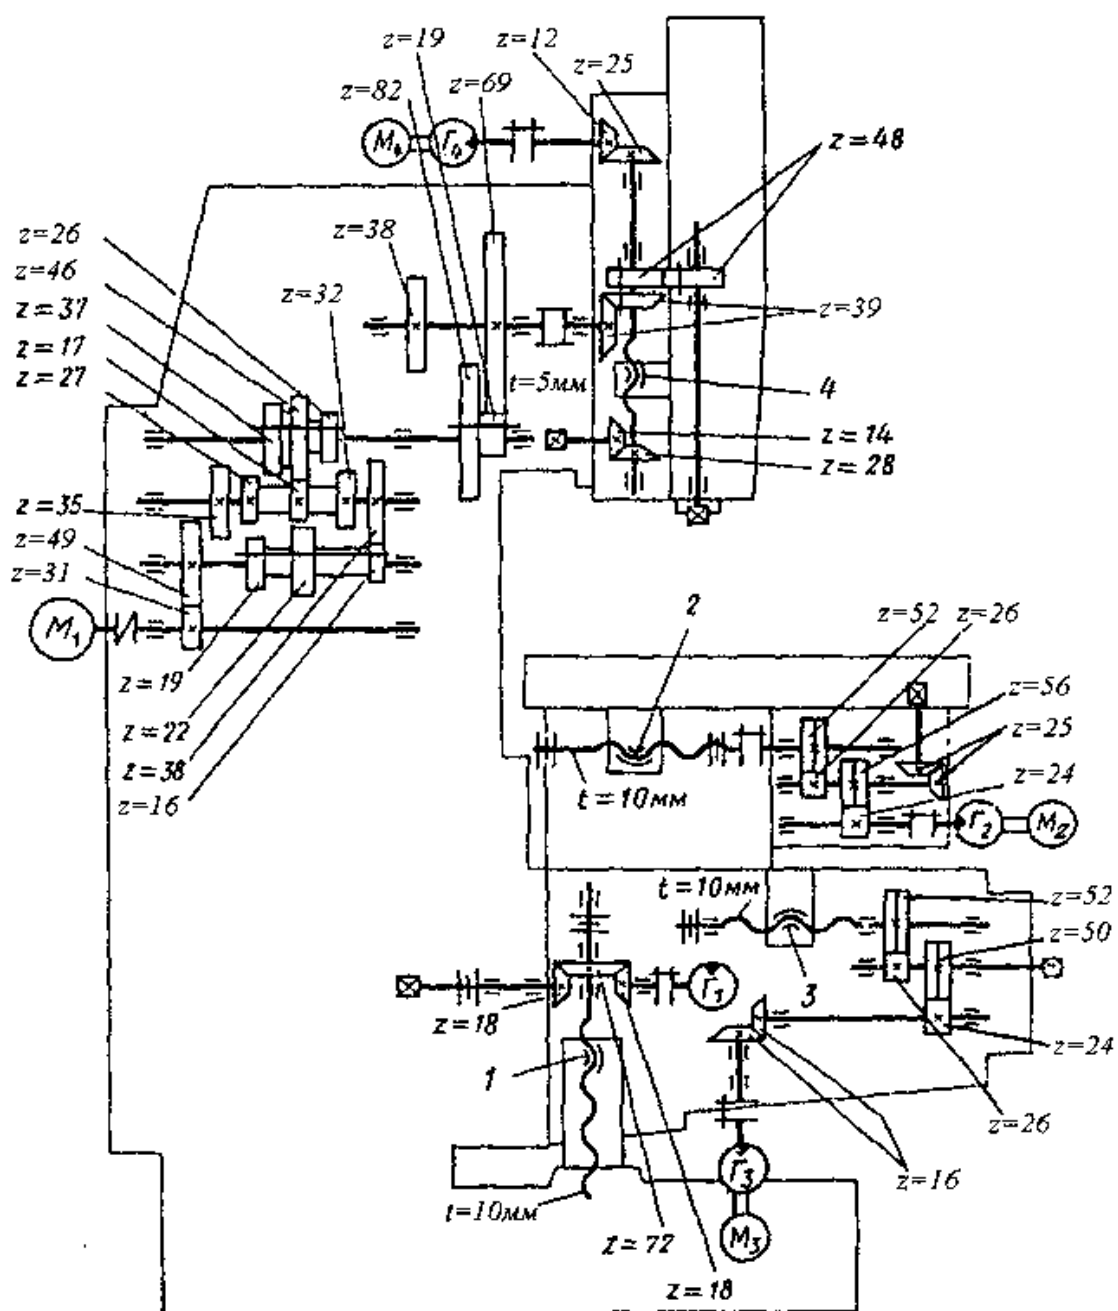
Кинематическая схема станка с ЧПУ 6P13Φ3
